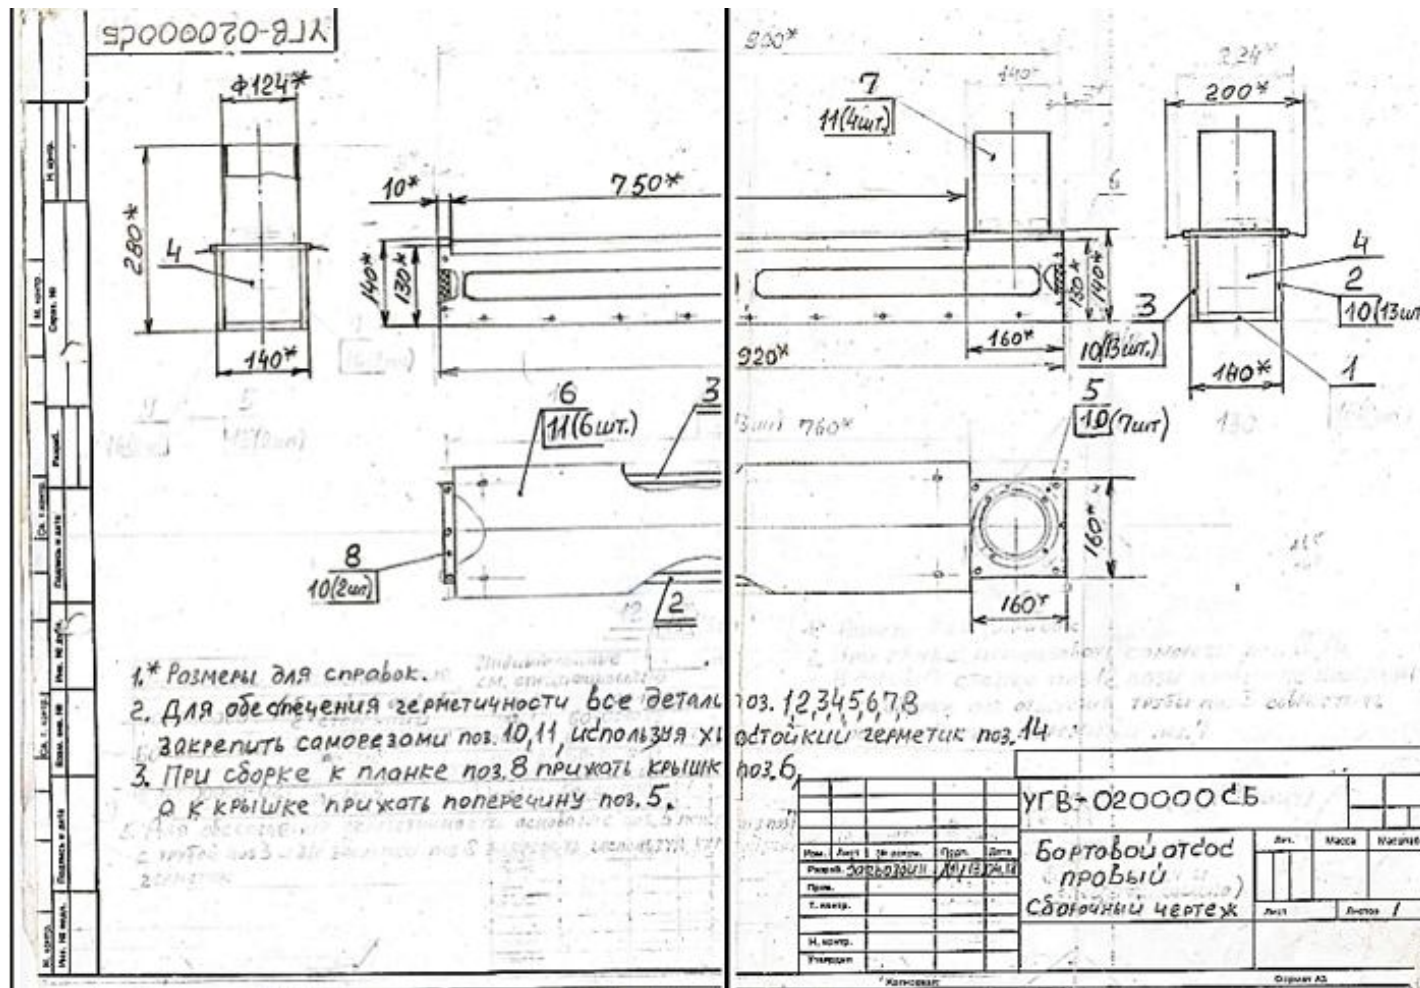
Сборочный чертеж на правый бортовой отсос
